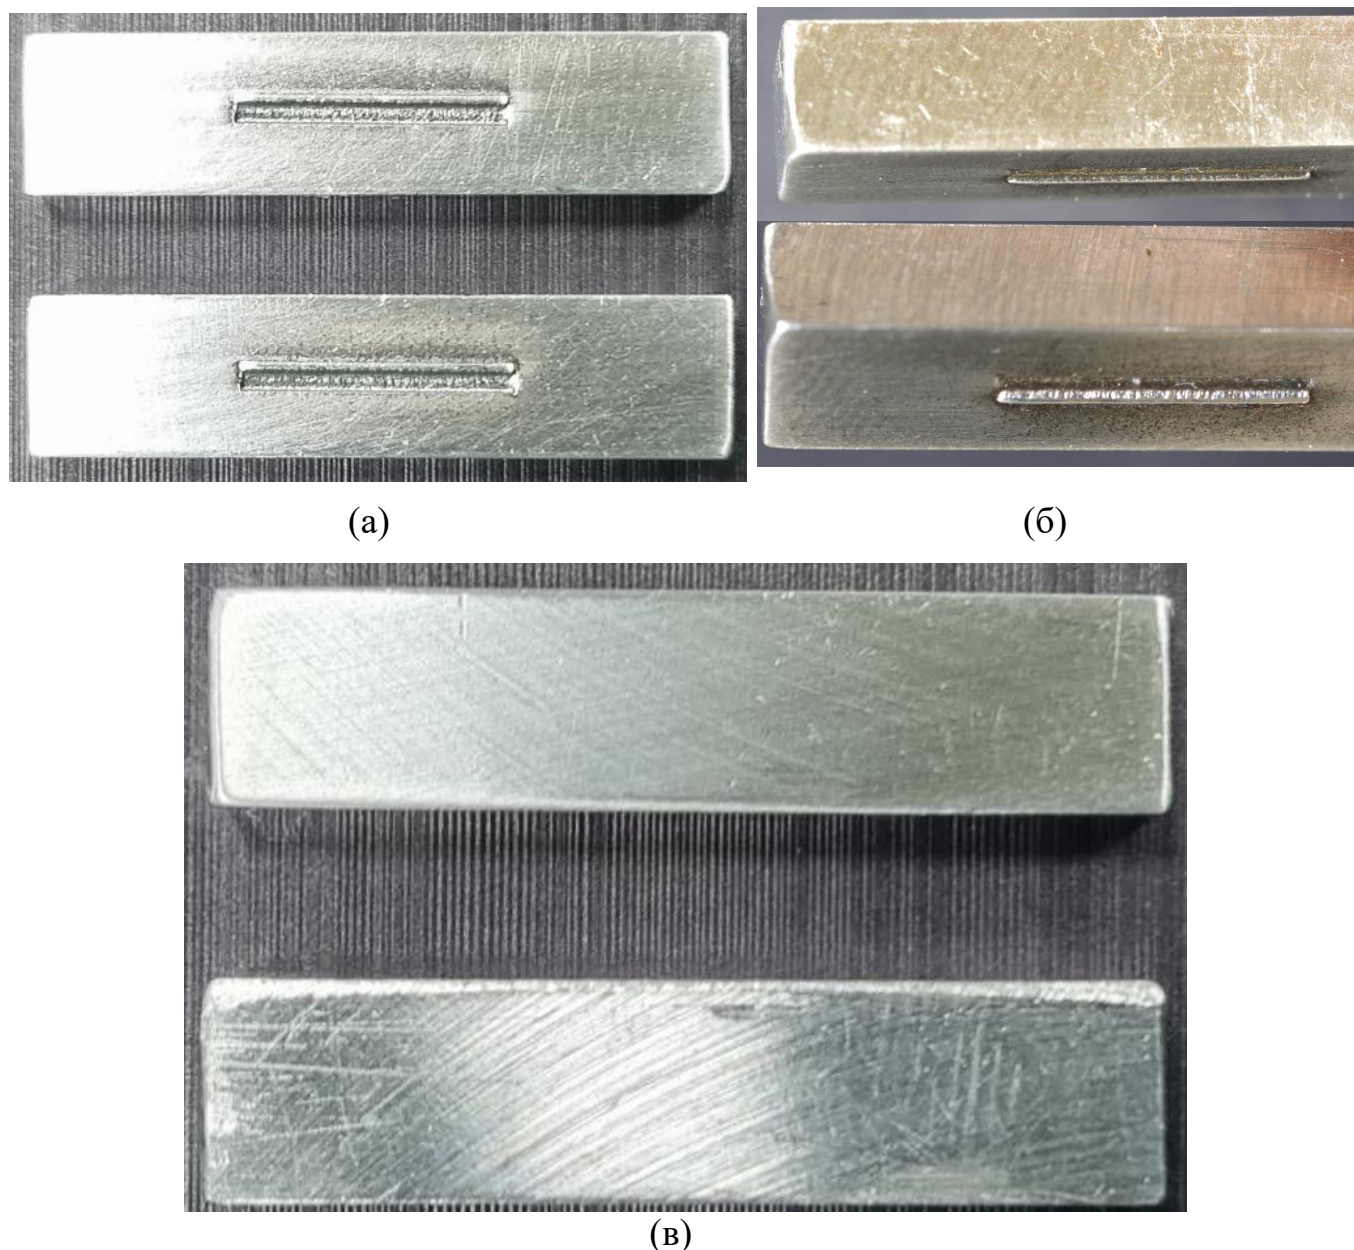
Внешний вид образцов, подготовленных для испытаний: а – образцы со сформированным выпуклым рельефом, вид сверху; б – образцы с нанесённым рельефом, вид сбоку; в – образцы в исходном состоянии [фото автора]
